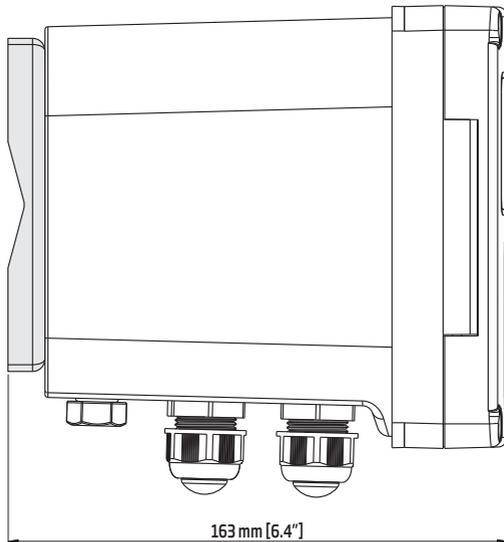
HI520 Controlador Fijado al Panel de Montaje en Pared
